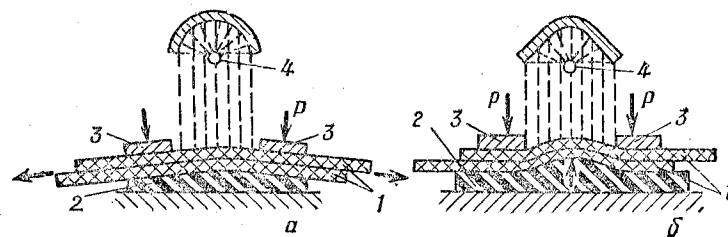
Схемы сварки ИК-излучением при создании давления; а — путем натяжения материала; б — за счет упругой подложки
